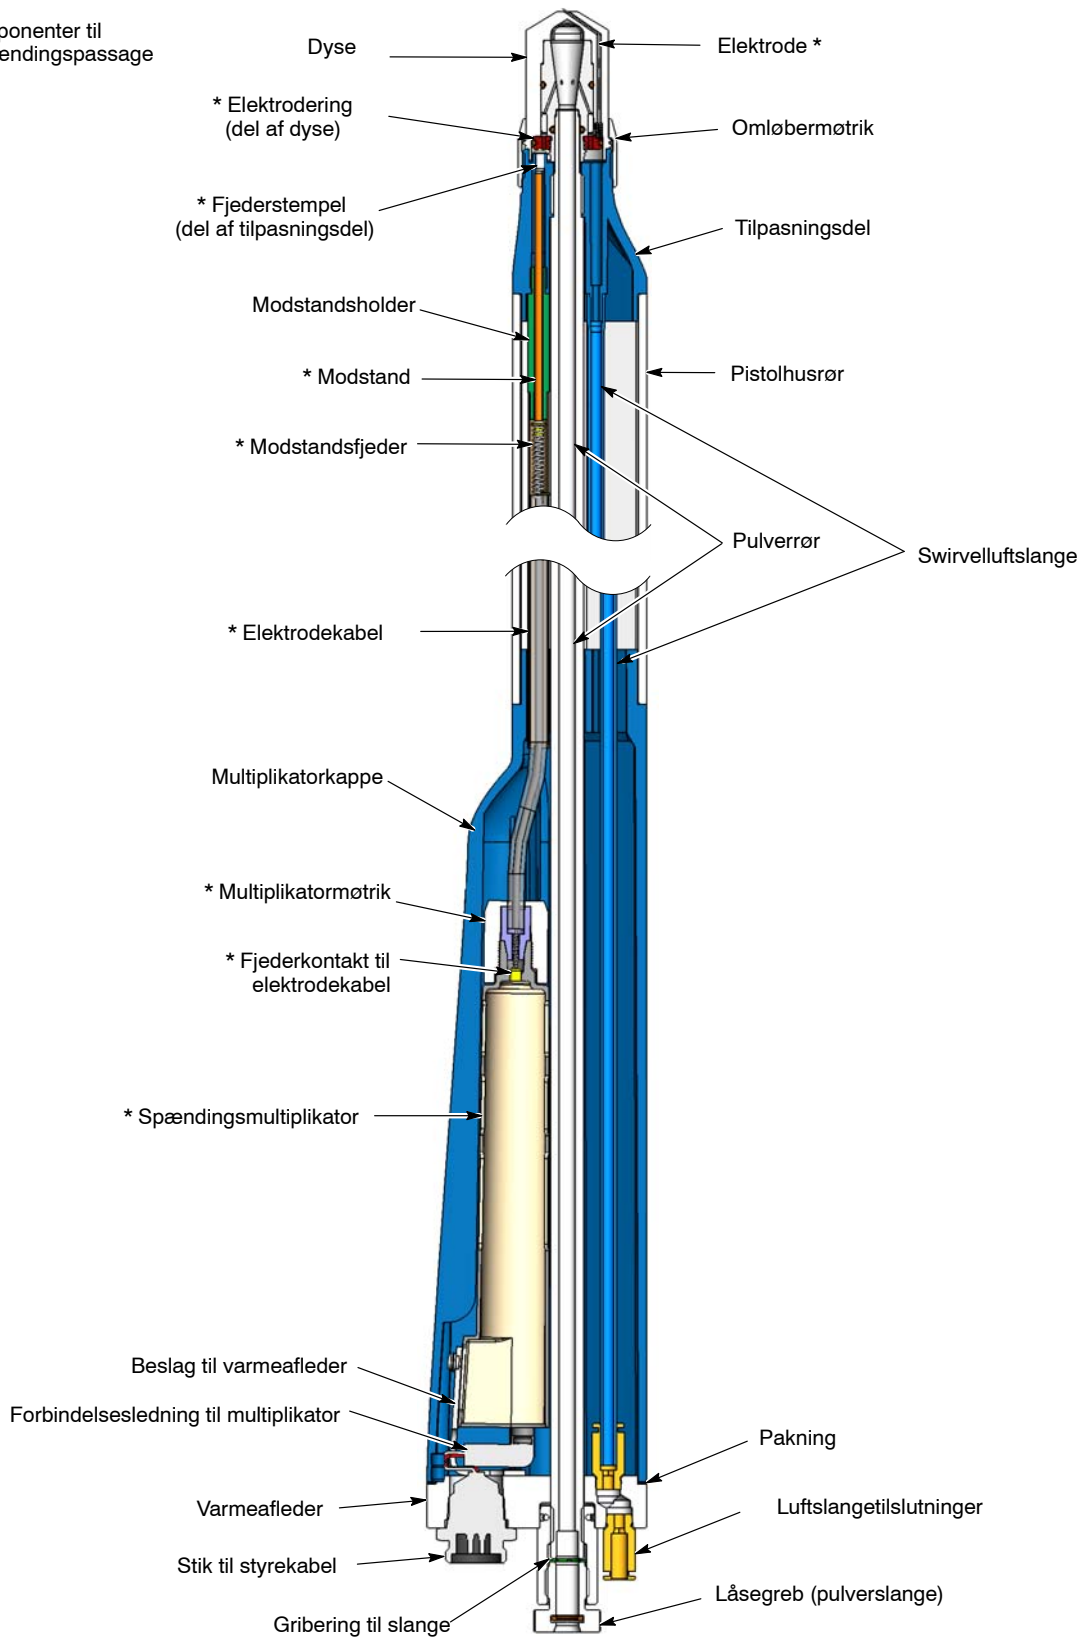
Tværsnit – Komponenter til pistol til rørmontering og pistolenhed
